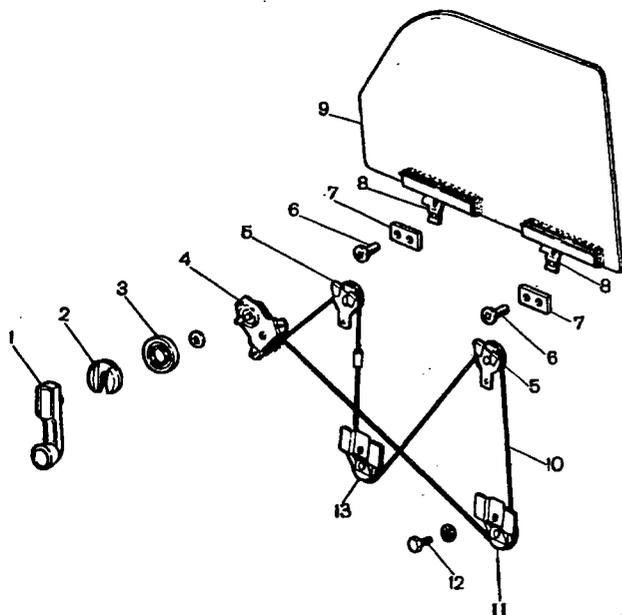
Привод переднего опускающего стекла: 1 - ручка стеклоподъемника; 2 - облицовка ручки стеклоподъемника; 3 - розетка ручки стеклоподъемника; 4 - механизм стеклоподъемника; 5 - верхние ролики; 6 - винты крепления прижимных пластин; 7 - прижимные пластины; 8 - кронштейны опускающего стекла; 9 - опускающее стекло; 10 - трос; 11 - нижний ролик; 12 - болт; 13 - натяжной ролик
